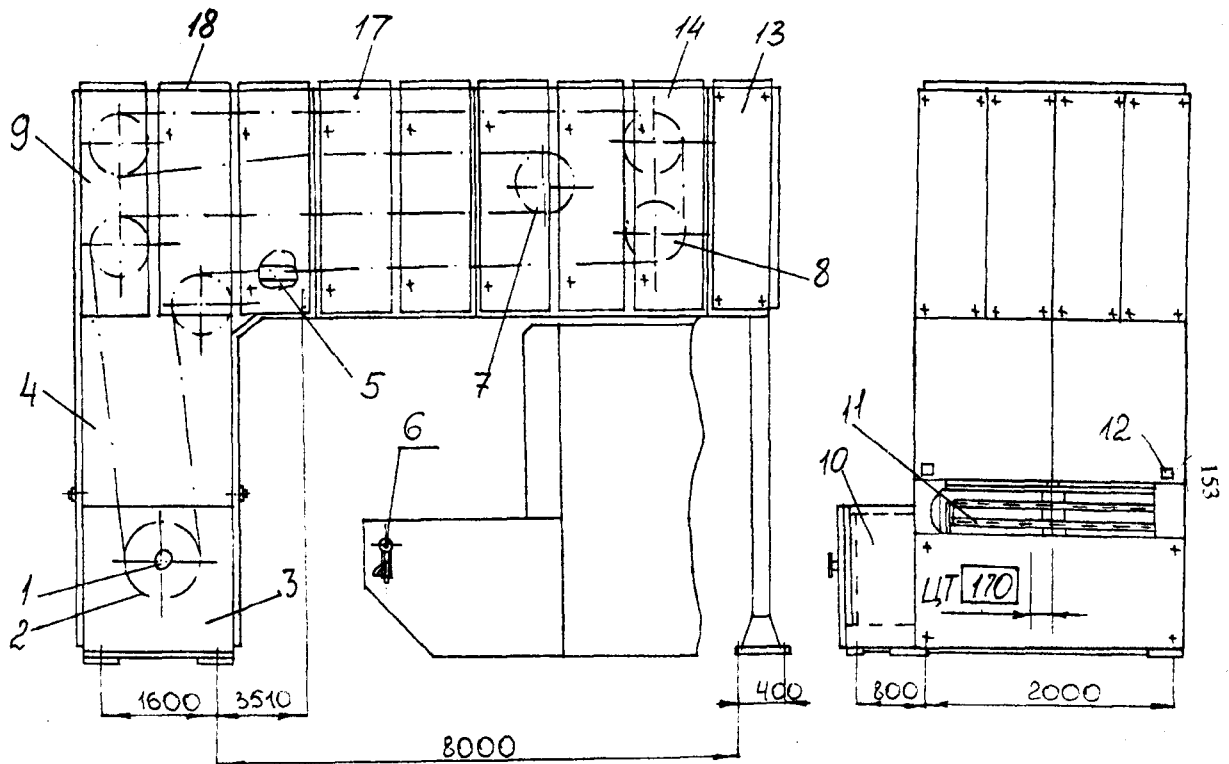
П2. Агрегат универсальный Г1-ХР-2А-30 для расстойки тестовых заготовок.
